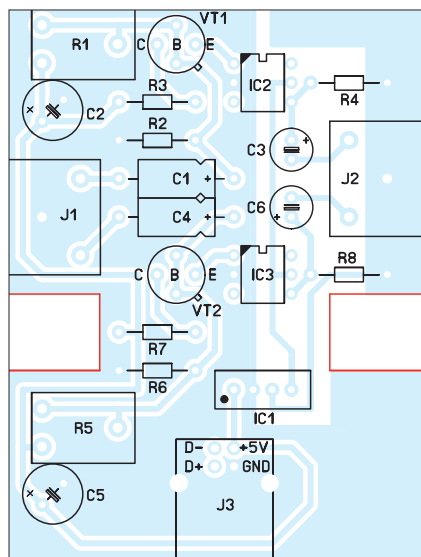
Bestückungsplan der Platine; je nach Gehäuse können die beiden rot markierten Aussparungen erforderlich sein.
